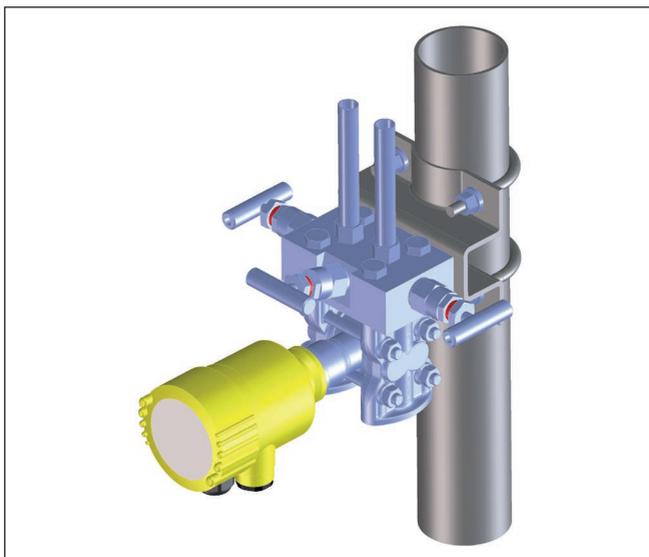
Exemplo de montagem suporte universal para blocos de válvulas
